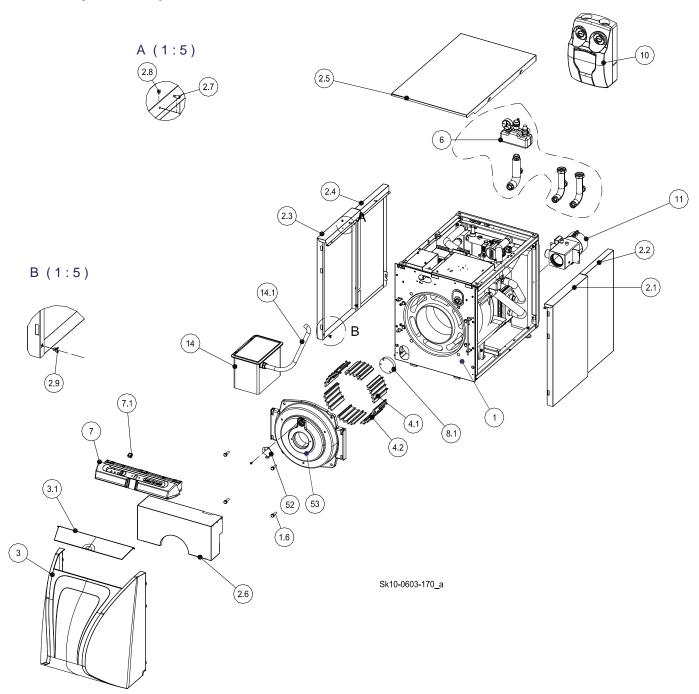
Sk10-0603-170_a EcoStar Hybrid komplett
